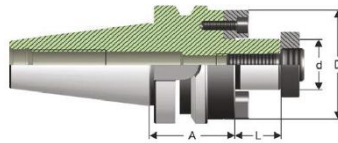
Оправка для торцевої фрези JIS B 6339 [15, С-12]
